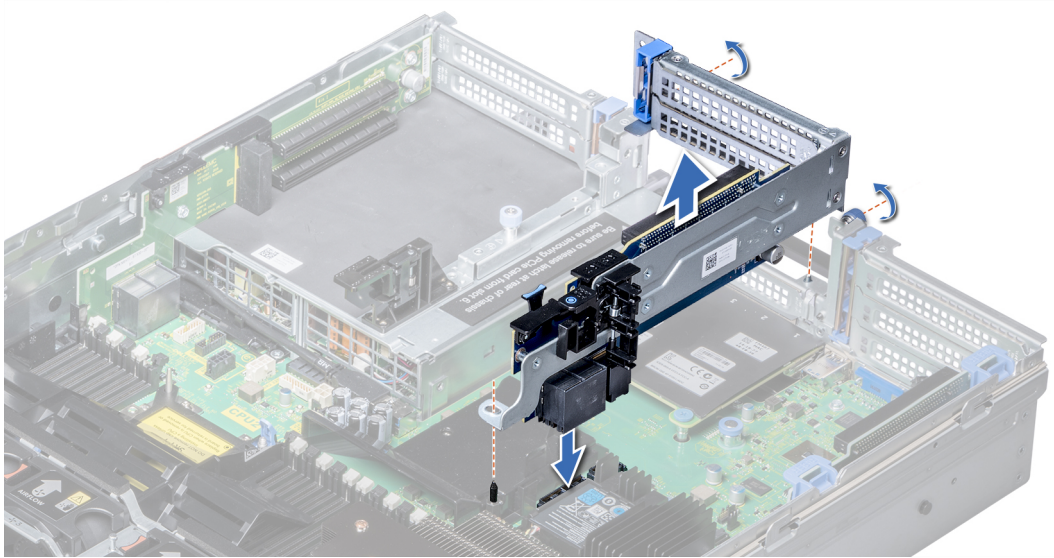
Installation de la carte de montage pour carte d'extension 2A
